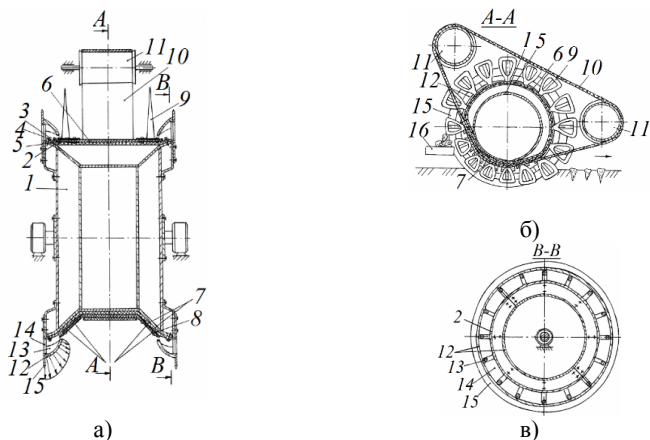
Выкапывающий рабочий орган корнеклубнеуборочной машины
